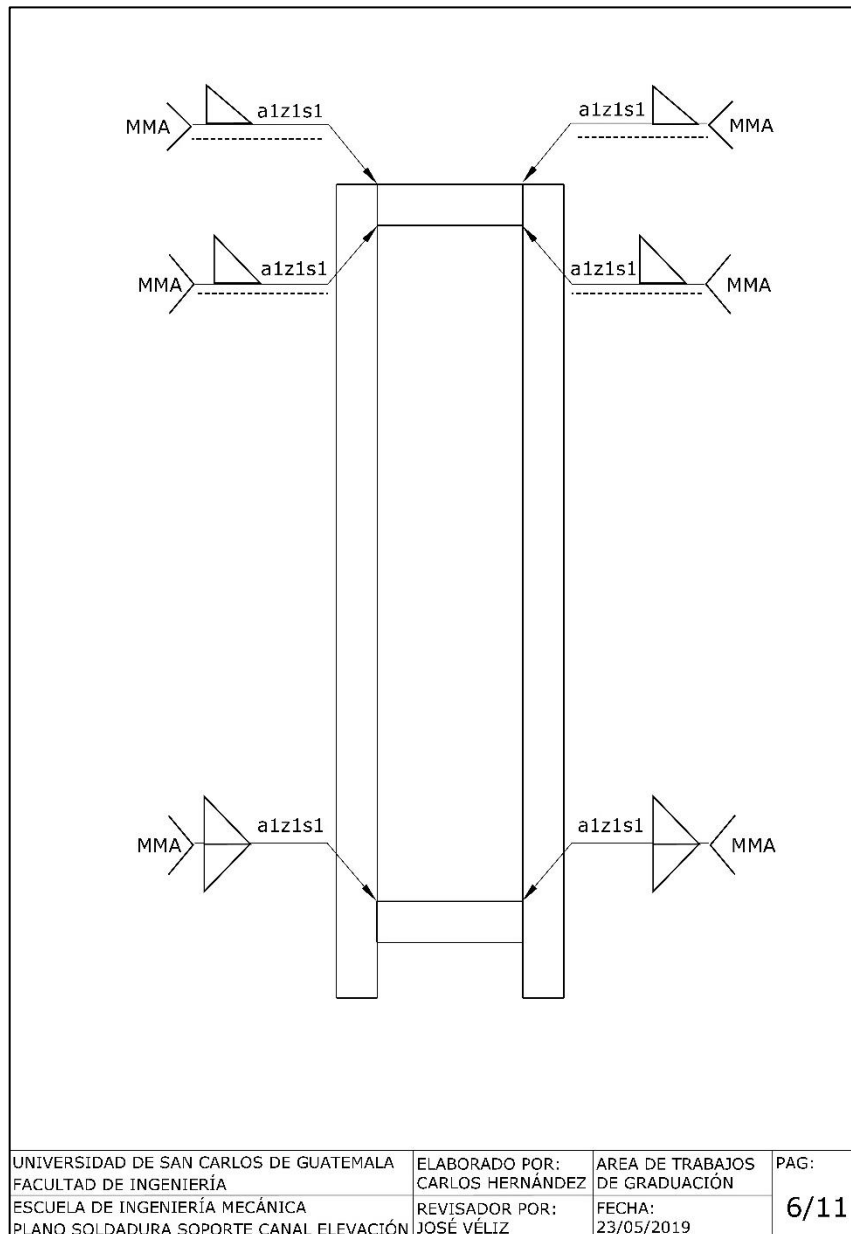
Plano de soldadura de soporte del canal vista planta
